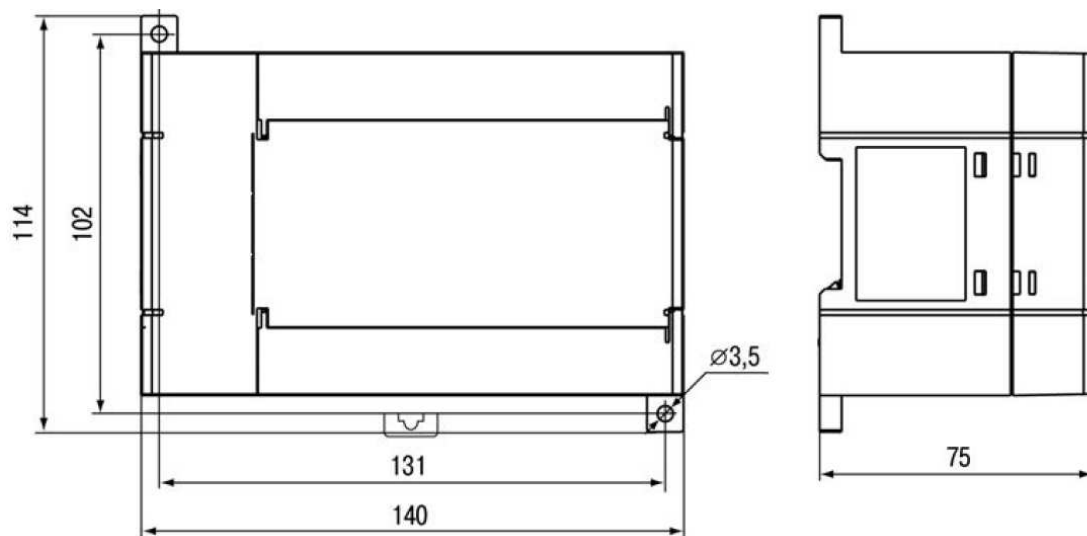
Габаритный чертеж модуля MB110-220.32ДН
